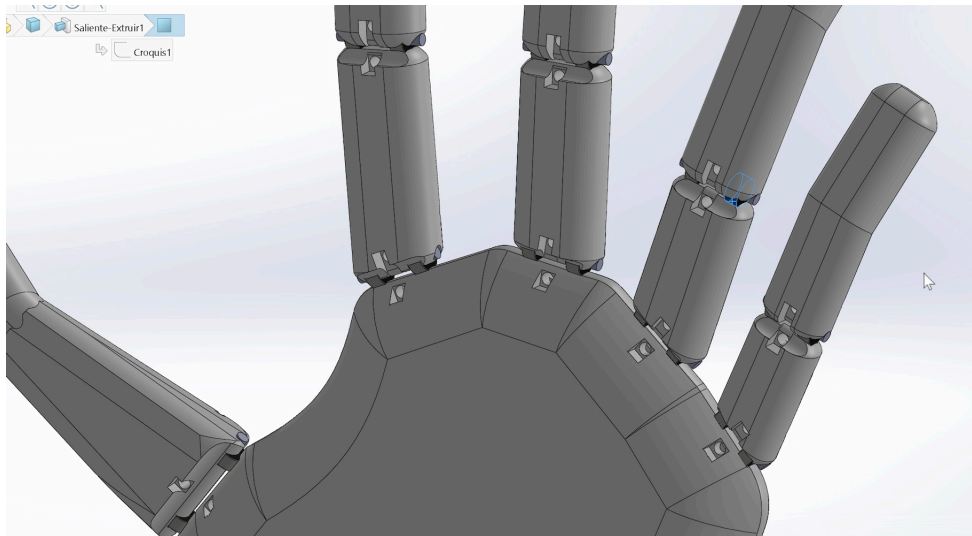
Diseño 3D palma y ensamble de los dedos vista posterior isométrica.
